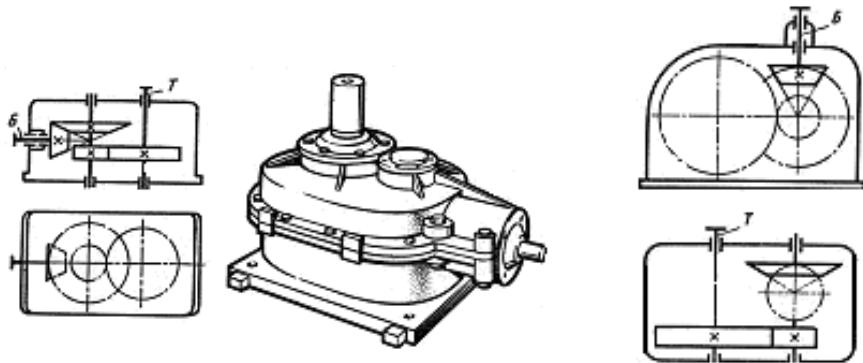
Коническо-цилиндрические редукторы
